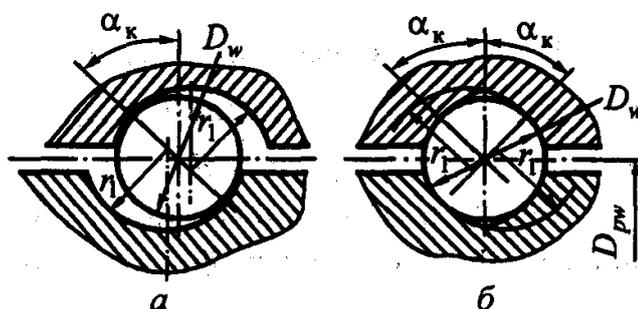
Профили резьбы: *a* — полукруглый; *б* — «стрельчатая арка»
